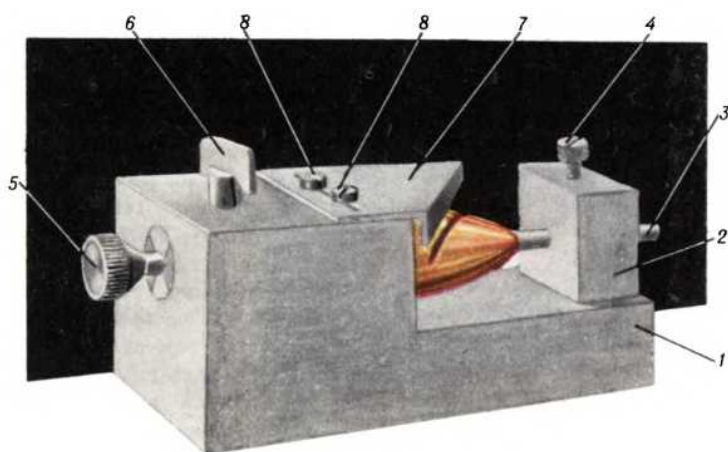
Пропиливание пазов в приспособлении: 1 — основание; 2 — стойка; 3 — подвижной упор; 4 — стопорный винт; 5 — упор с делительной головкой; 6 — фиксатор; 7 — сменный шаговый угольник; 8 — крепежные винты.
